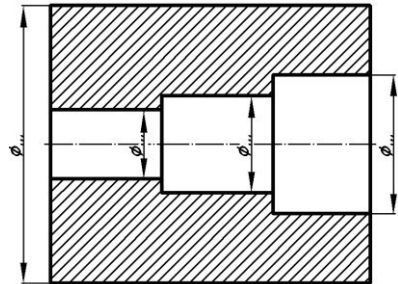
Вибір головного виду для деталі, яка обмежена ступінчастими циліндричними поверхнями
